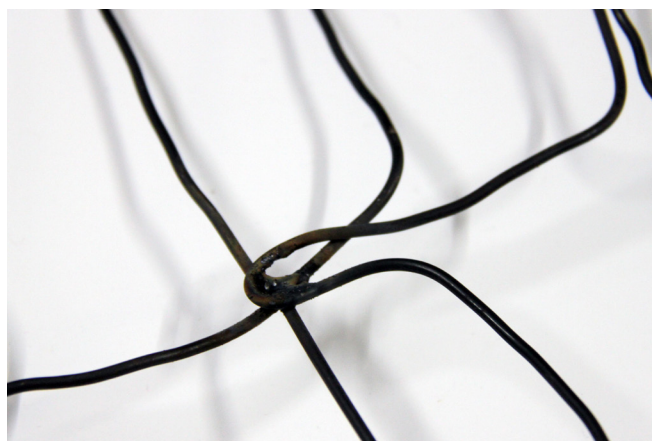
Pormenor da soldadura da letra *f*.
